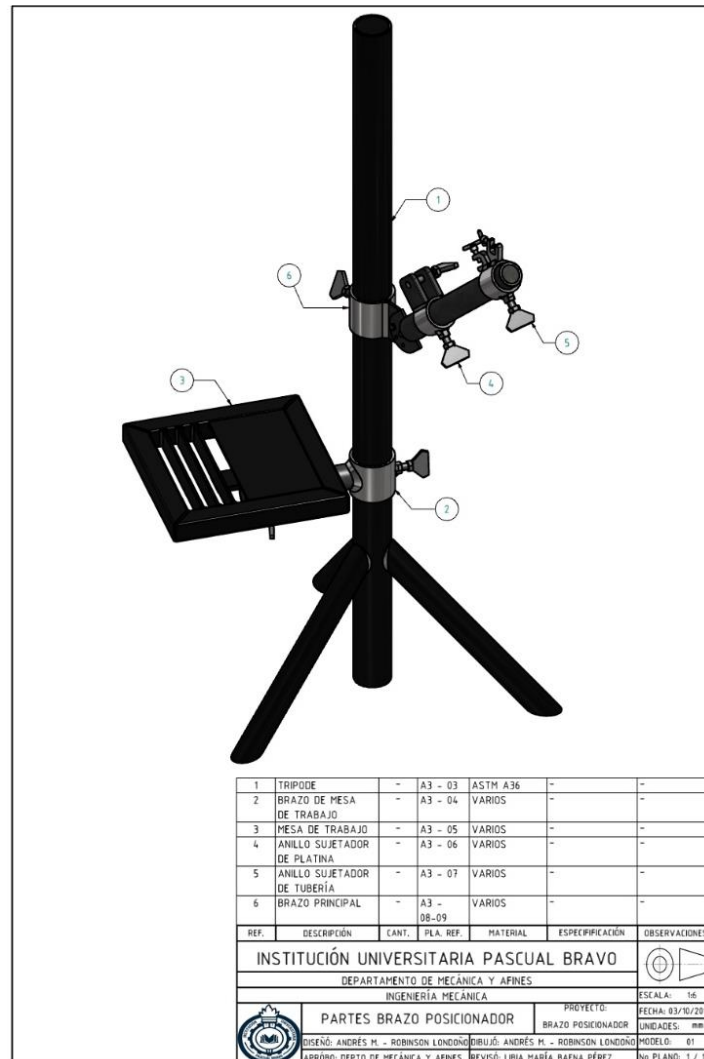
Ensamble y Lista de Partes Brazo Posicionador
